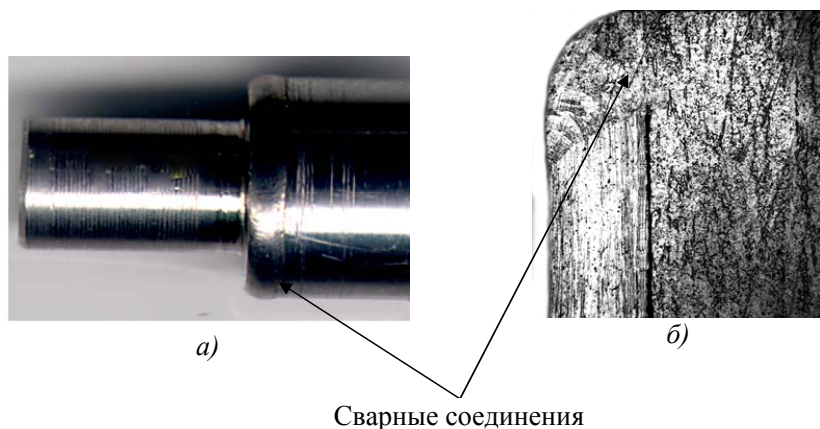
Внешний вид (а, $\times 5$) и сечение (б, $\times 50$) сварного соединения оболочки из дисперсионно-упрочненной стали твэла экспериментальной ТВС РУ БОР-60, выполненного лазерной сваркой
